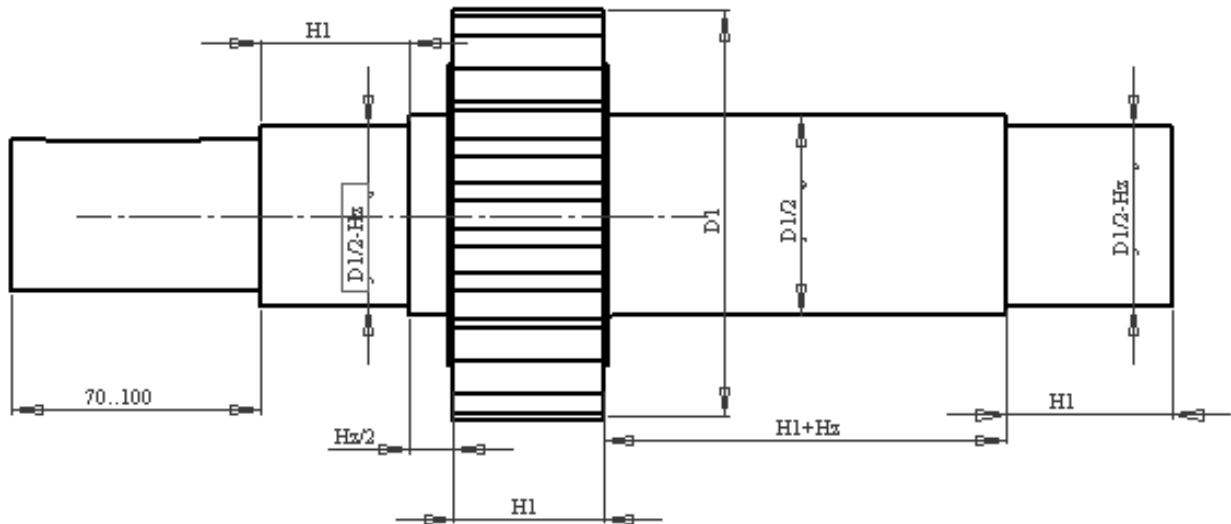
Примерные значения основных размеров вала-шестерни
